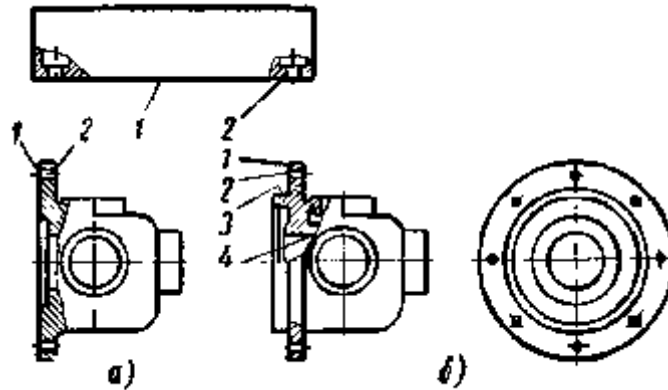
Базові поверхні корпусних деталей:
